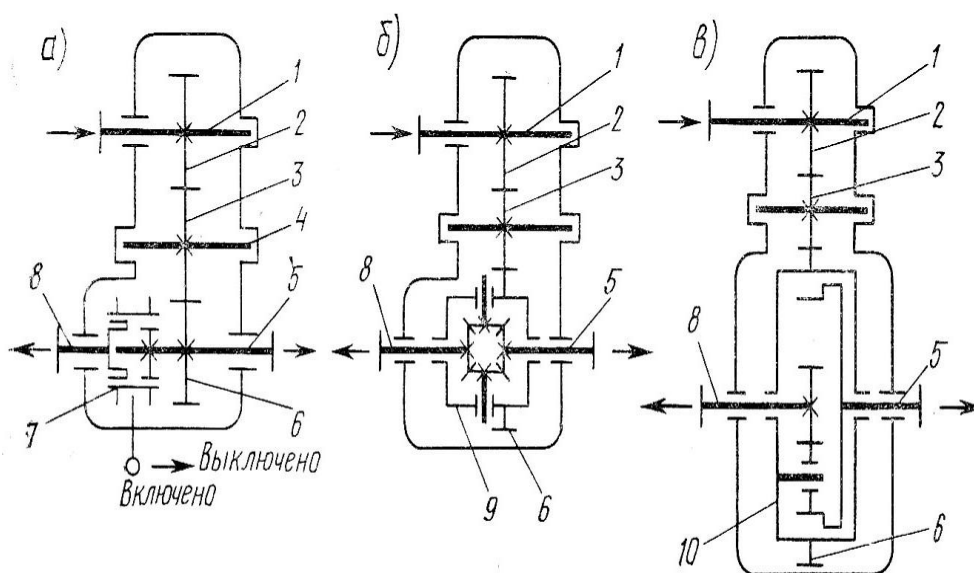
Кинематические схемы раздаточных коробок: а – с блокированным приводом; б,в – с дифференциальным приводом; 1 – ведущий вал; 2 – ведущая шестерня; 3 – промежуточная шестерня; 4 – промежуточный вал; 5 – вал привода заднего моста; 6 – ведомая шестерня; 7 – муфта включения; 8 – вал привода переднего моста; 9 – симметричный дифференциал; 10 – несимметричный дифференциал
